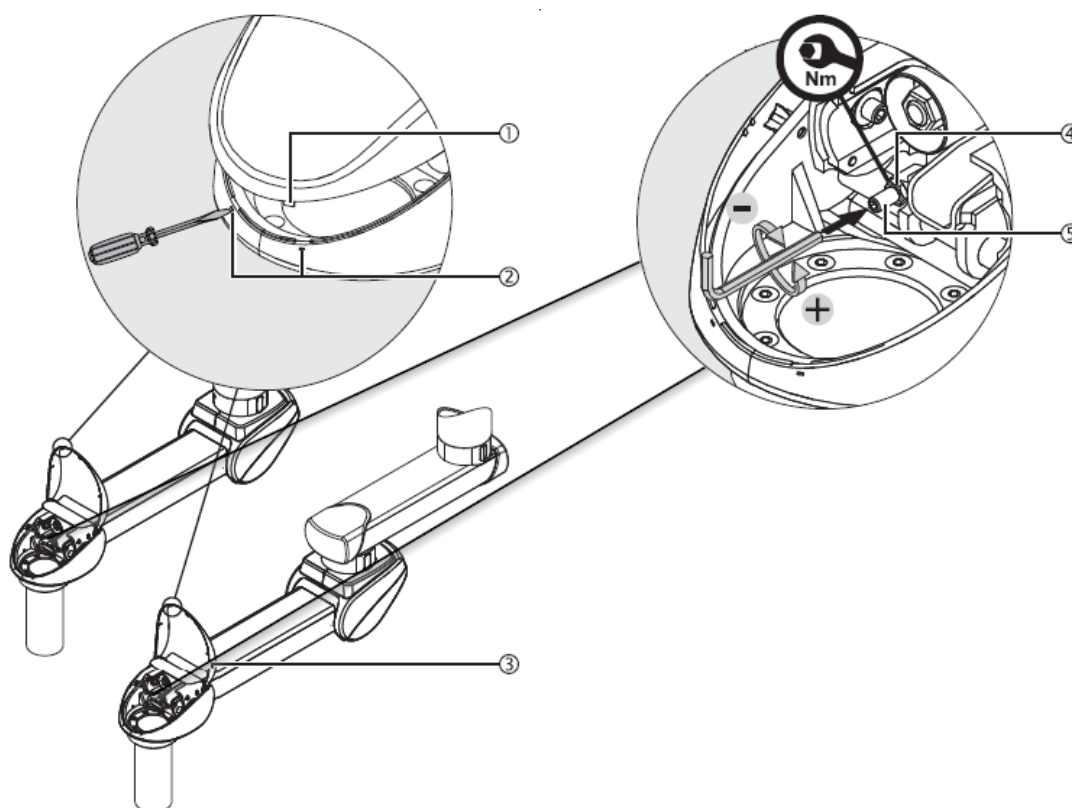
Réglage de l'élévation verticale sur un bras à ressort
